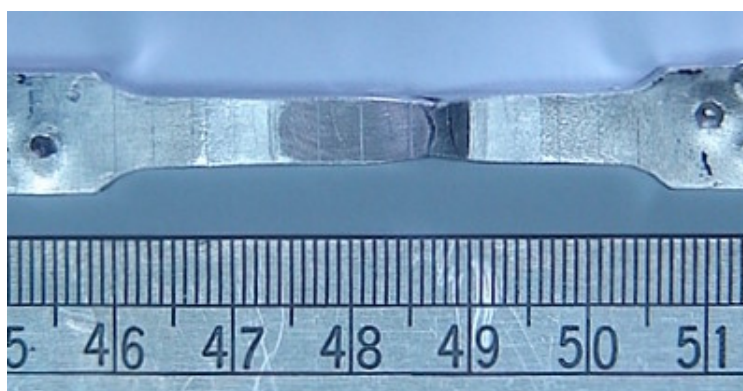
Ruptura sobre o cordão de solda FSW - geometria cônica com rosca.
